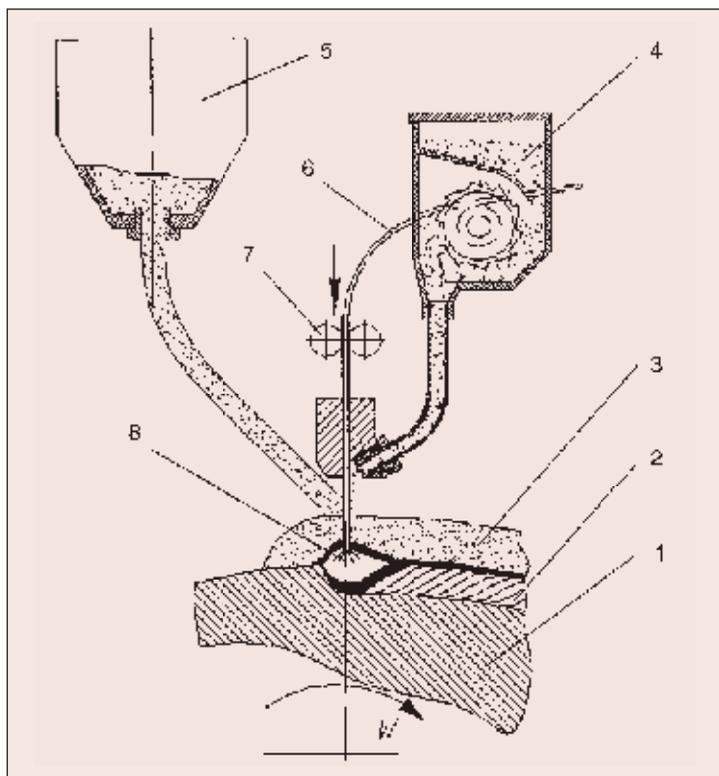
Схема наплавки под слоем флюса с подачей металлического порошка: 1 — наплавляемая деталь; 2 — наплавленный валик; 3 — слой флюса; 4 — устройство подачи порошка; 5 — бункер с флюсом; 6 — электродная проволока; 7 — подающие ролики; 8 — электрическая дуга
